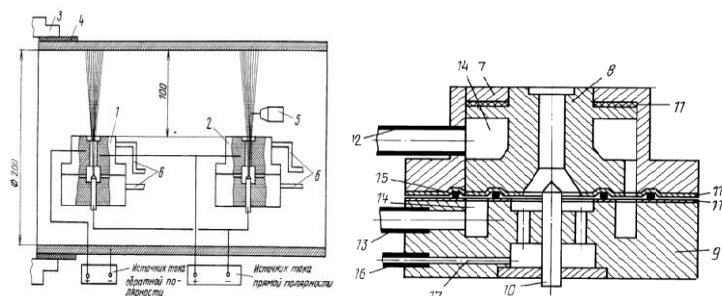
Устройство для нанесения порошковых покрытий на внутренние поверхности цилиндрических изделий:
